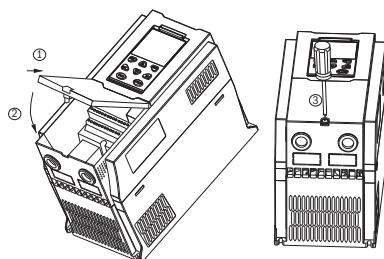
Снятие и установка крышки габариты 8÷9 (110÷160 кВт) (лист 1 из 2)
